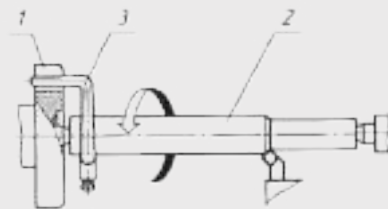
Кріплення довгої заготовки у центрах з використанням токарного хомутика: 1 — планшайба; 2 — заготовка; 3 — токарний хомутик
